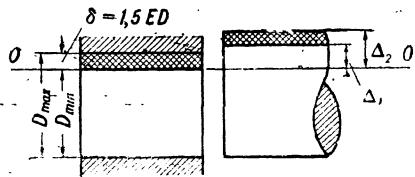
Допуски на диаметры оправки и изделия.
